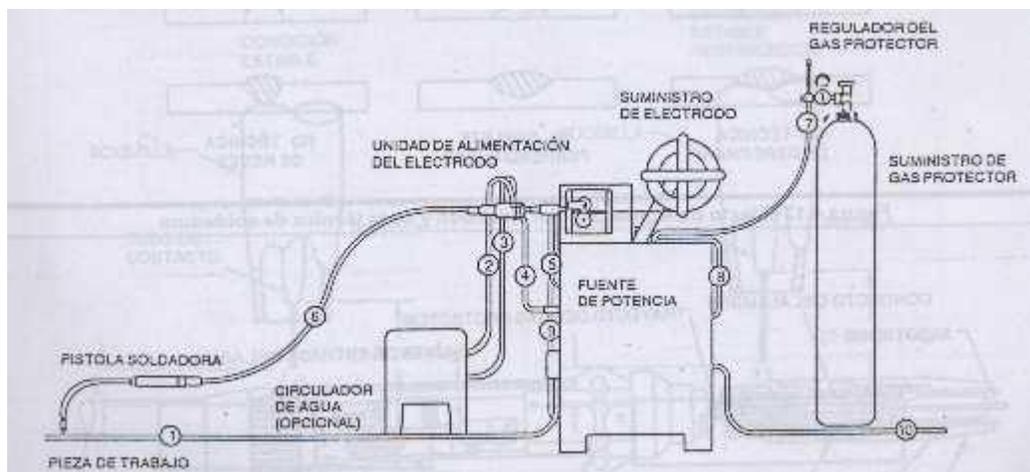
Diagrama del equipo para soldadura por arco de metal y gas.¹⁸
